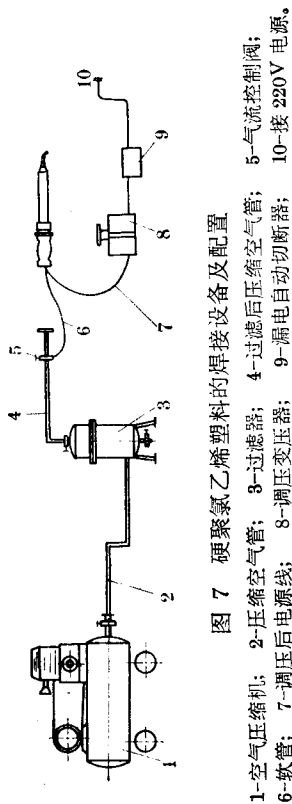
硬聚氯乙烯塑料的焊接设备及配置
